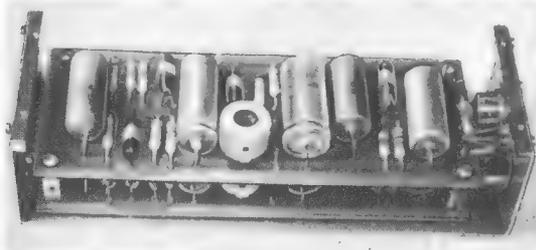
In einem Gehäuse sind zwei gleichartige Entzerrer für einen Stereo-Tonabnehmer zusammengebaut. Die Maße sind so klein, daß man es unter das Plattenspieler-Chassis montieren kann
